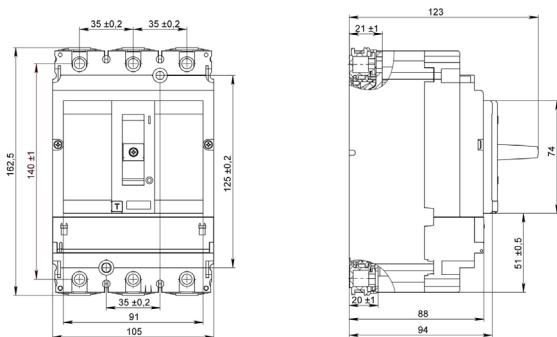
Габаритные, установочные и присоединительные размеры выключателей
